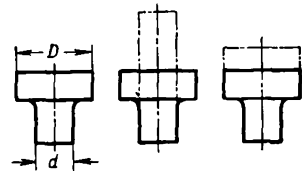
Способы штамповки фланцевой втулки: а — высадкой; б — выдавливанием
